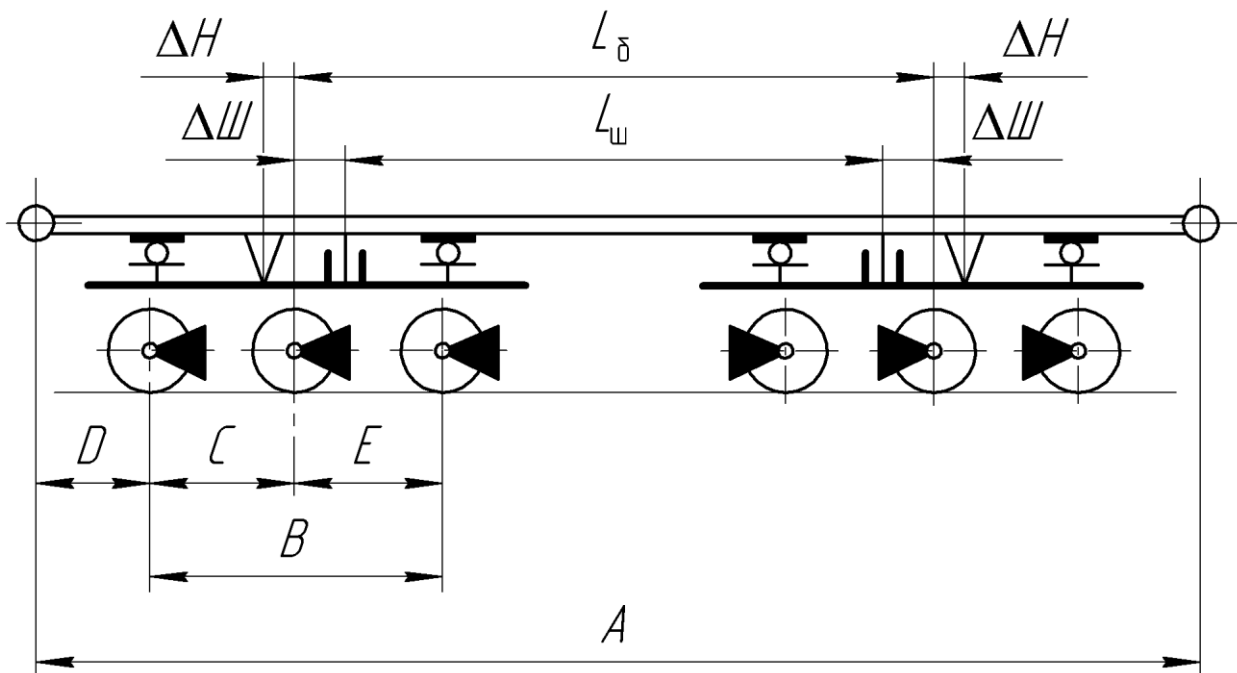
Схема екіпажної частини з тривісними безщелепними візками II групи з опорно-повертаючими пристроями роликового типу і опорно-осьовим підвішуванням ТЕД
